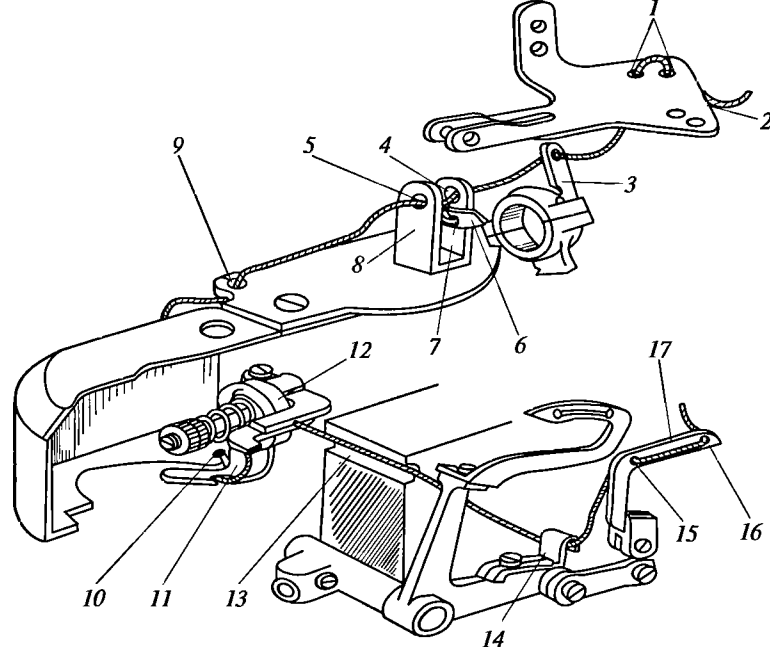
Схема заправки нитки нижнего петлителя в швейной машине класса 51
